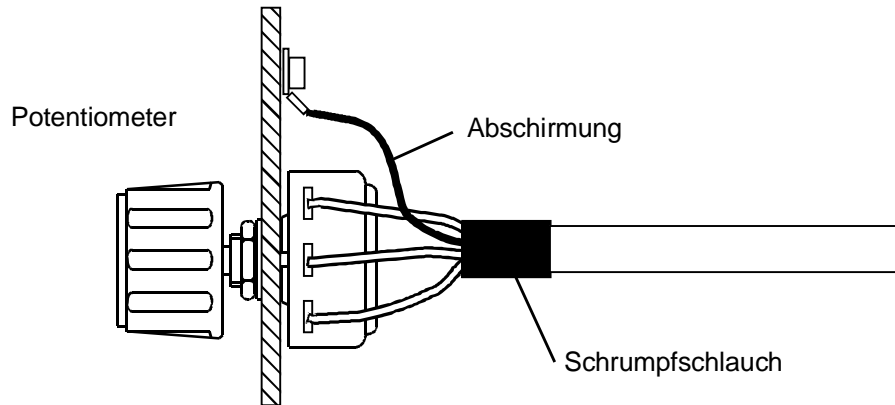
Beispiel einer Schirmbefestigung ohne Stecker
